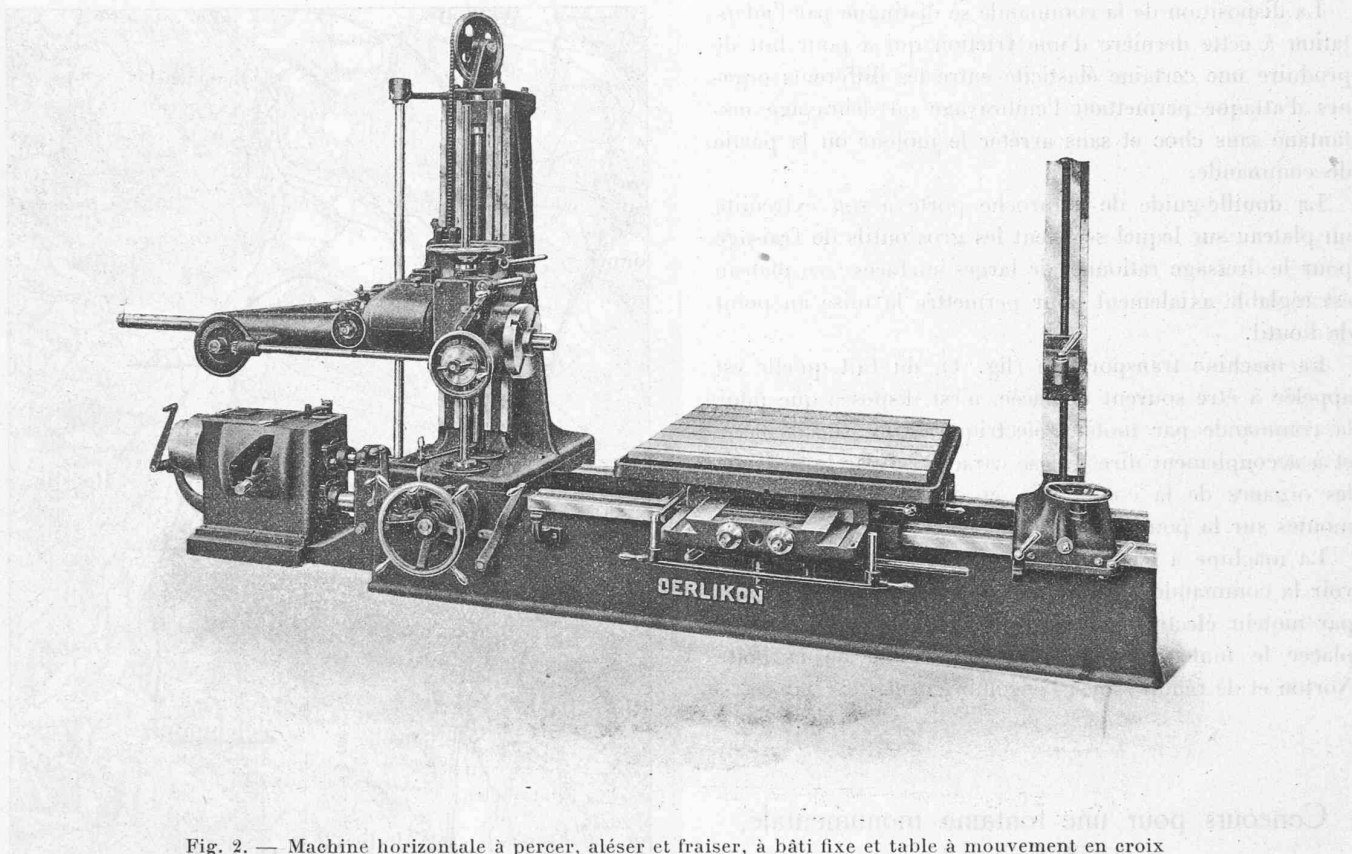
Machine horizontale à percer, aléser et fraiser, à bâti fixe et table à mouvement en croix avec broche de 80 mm. de diamètre.
